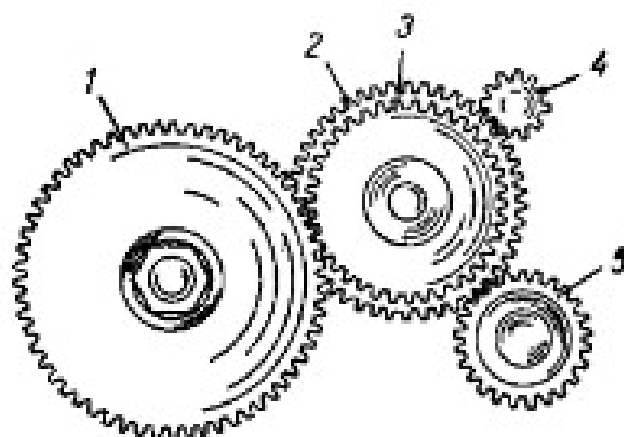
Шестерни привода коленчатого вала пускового двигателя:
